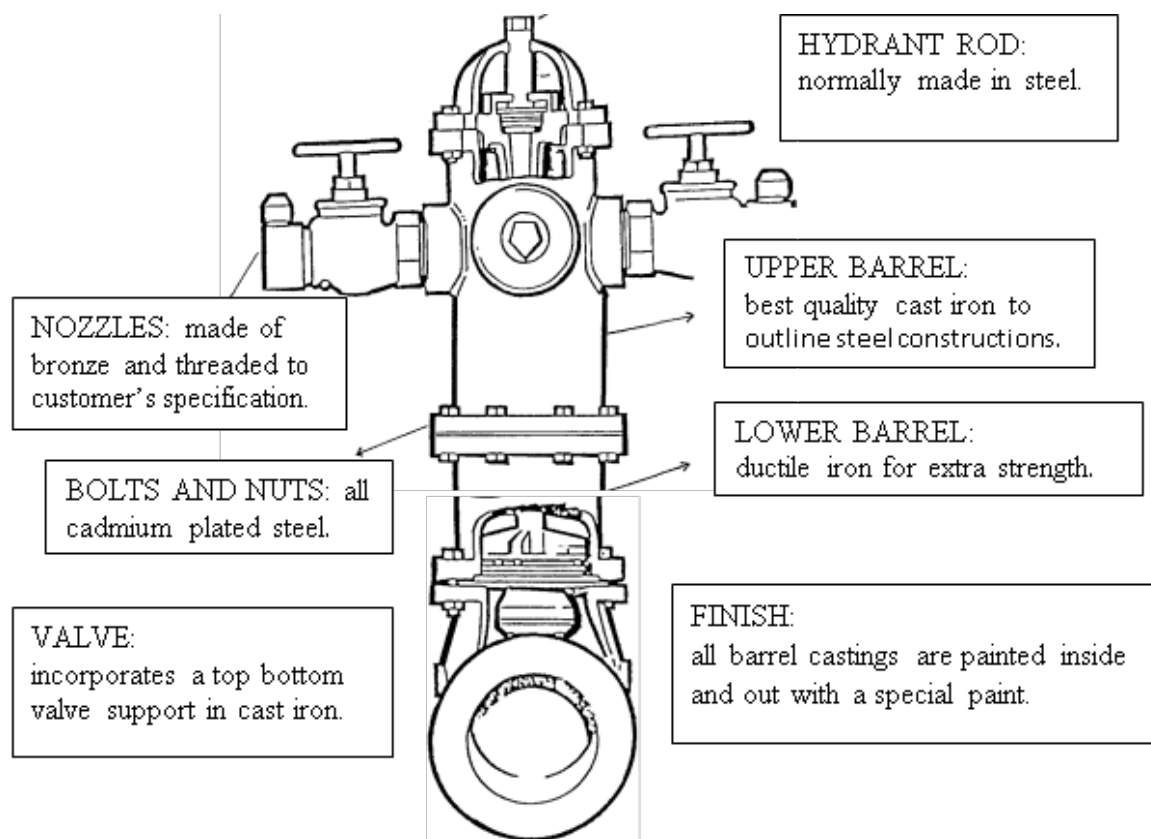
Схема пожарного гидранта [4]. Конструкция: 1 — шток гидранта: обычно производится из стали; 2 — верхний корпус: металлоконструкция из чугуна наилучшего качества; 3 — нижний корпус: ковкий чугун для высокой прочности; 4 — финишная обработка: все металлические корпуса окрашиваются изнутри и снаружи специальной краской; 5 — вентиль: включает нисходящий клапан, сделанный из чугуна; 6 — болты и гайки: кадмированные, из стали с защитным слоем; 7 — водораспыляющие насадки: производятся из бронзы с резьбой по техническим требованиям заказчика.
